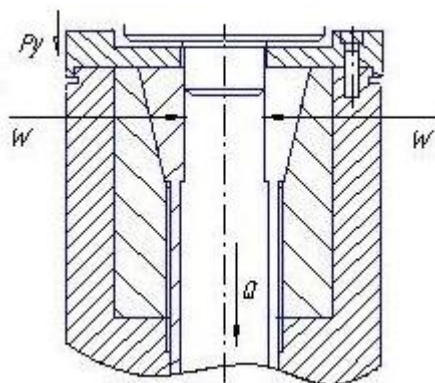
Схема закрепления заготовки в цанговом патроне
